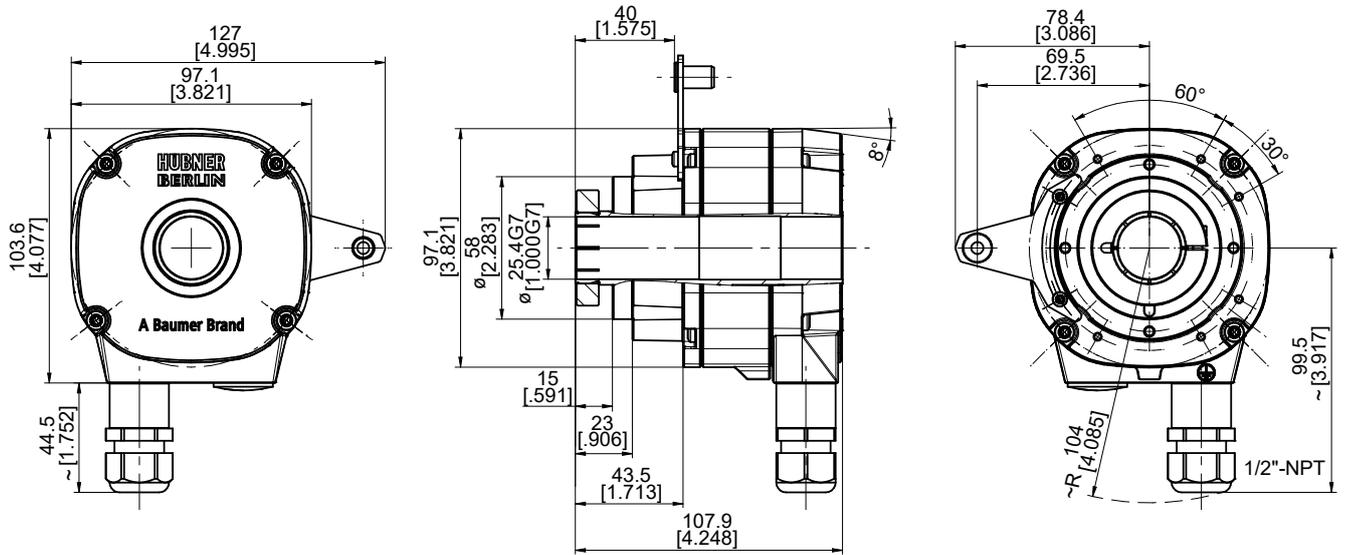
Abmessungen der einseitig offenen Hohlwelle (Abmessungen in mm und [Inch])
